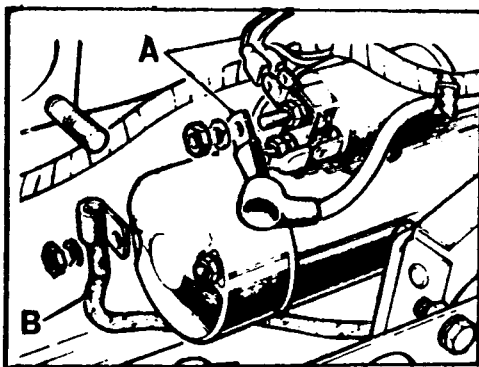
Desmontaje de cables de alimentación del motor y cable de masa
